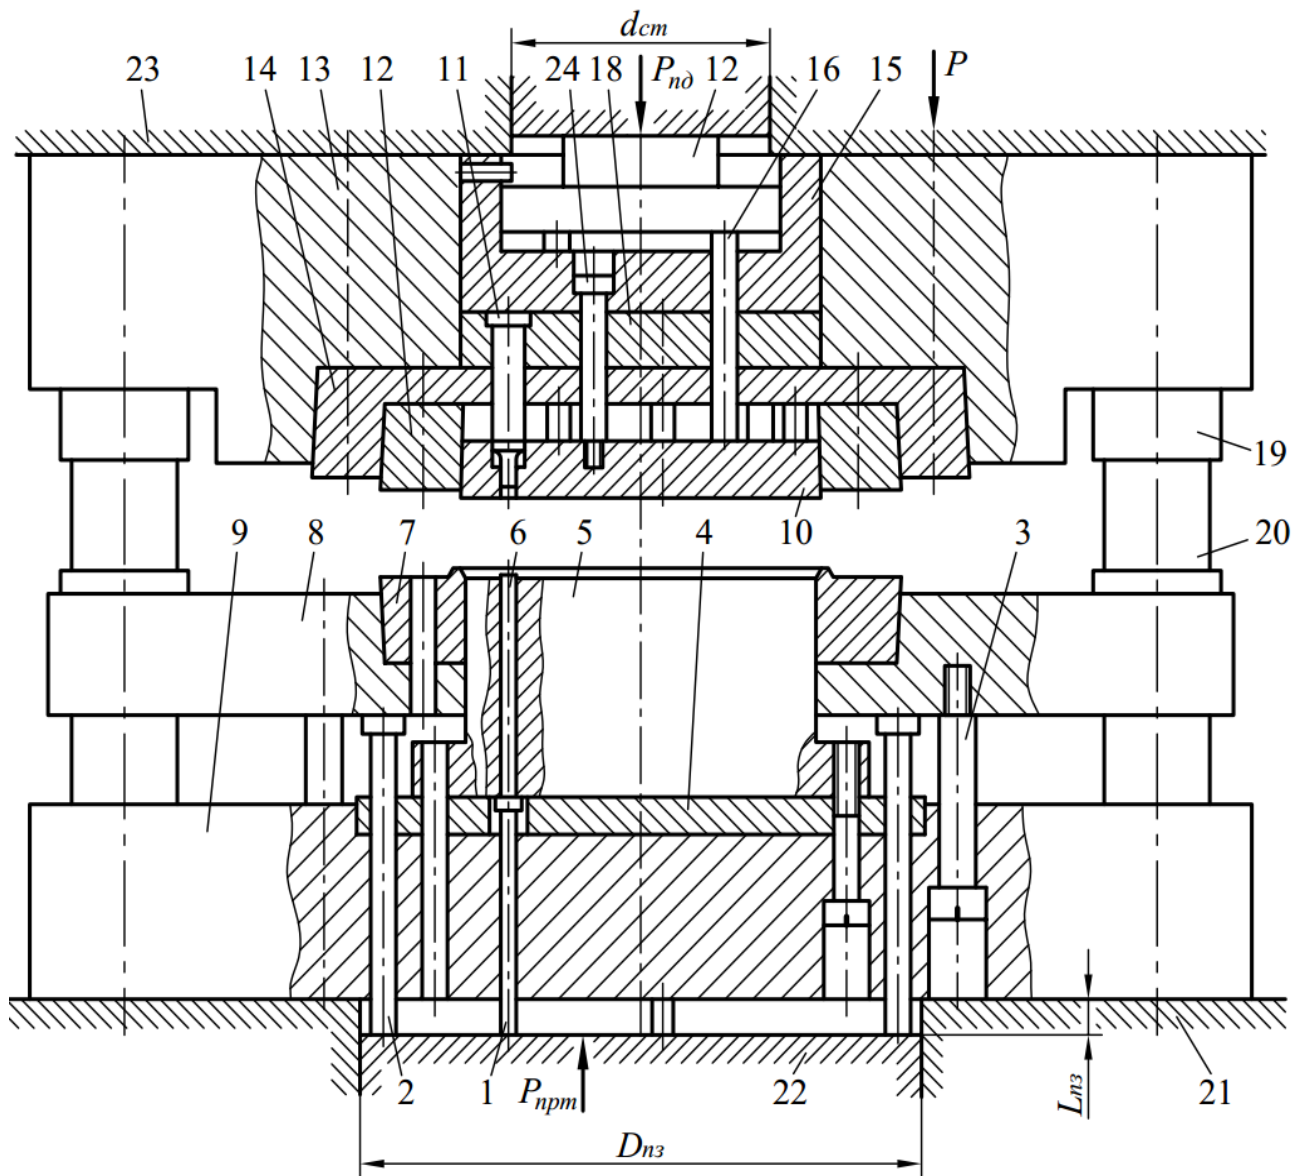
Схема штампа з нерухомою пуансон-матрицею і рухомих притискувачем: 1 – штовхачі; 2 – штовхачі; 3 – гвинт; 4 – прокладка; 5 – пуансон-матриця; 6 – виштовхувачі; 7 – притискувач; 8 – плита проміжна; 9 – плита нижня; 10 – виштовхувач; 11 – пуансони; 12 – матриця; 13 – плита верхня; 14 – обойма; 15 – опора; 16 – штовхачі; 17 – підп’ятник; 18 – пуансоноутримувач; 19 – втулка напрямна; 20 – колонка напрямна; 21 – повзун преса; 22 – притискувальний плунжер преса; 23 – стіл преса; 24 – гвинти
